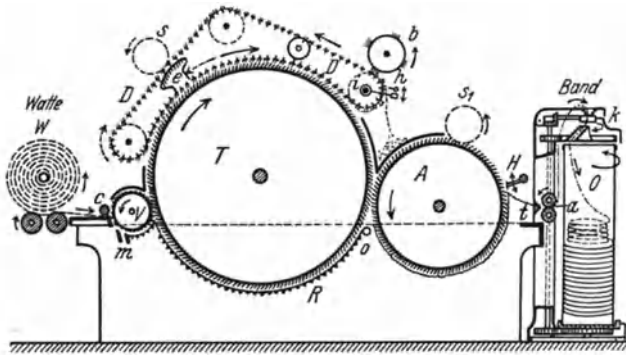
Schema einer Deckelkrempel mit wandernden Deckeln.
